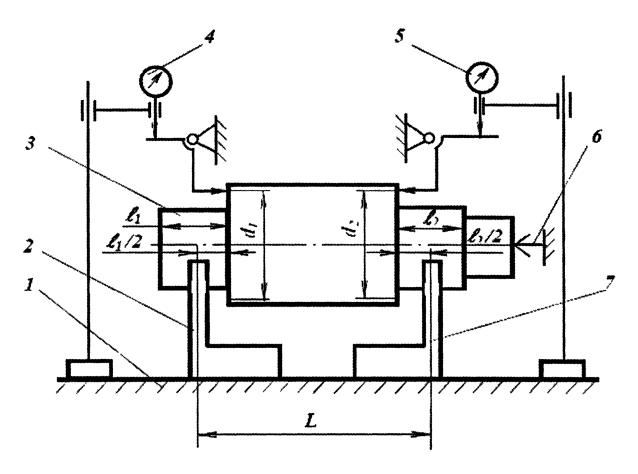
Схема измерения торцового биения заплечиков вала относительно общей оси шеек под подшипники: I – поверочная плита; 2 и 7 – ножевидные призмы; 3 – измеряемая деталь; 4 и 5 – индикаторы часового типа; δ – упор
